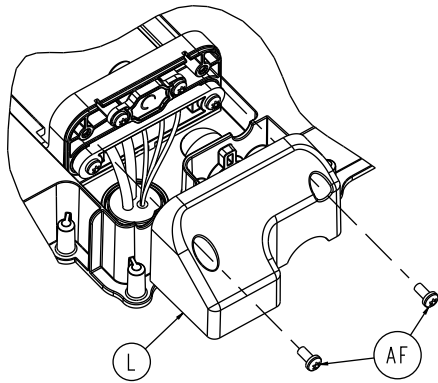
Retirer les vis du couvercle arrière du support de batterie
